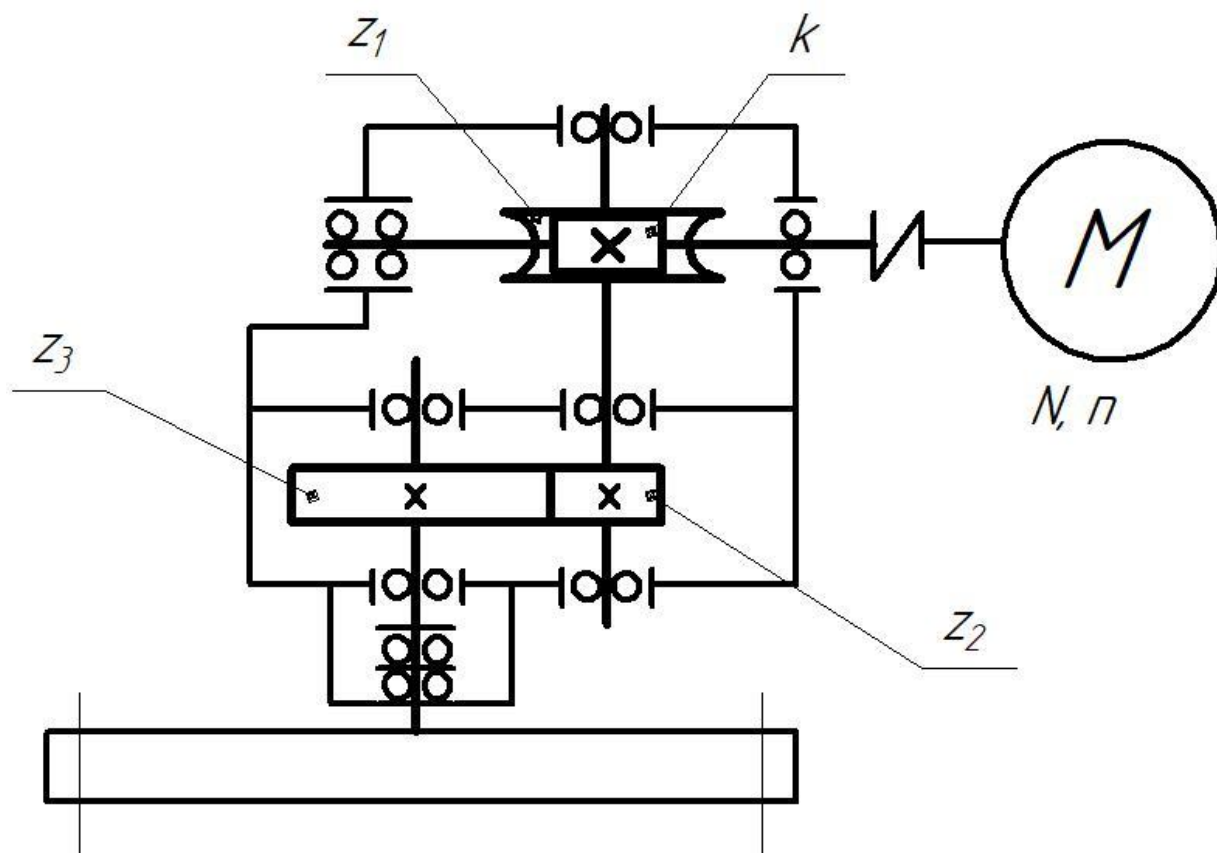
Кінематична схема приводу інструментального магазину
